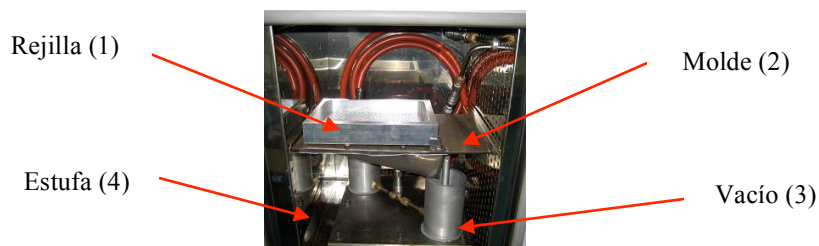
TP-RTM para fabricar placas de composite pCBT-SMA.
